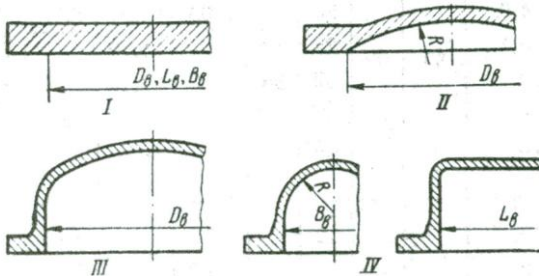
Основные типовые конструктивные формы крышек, применяемых в химических аппаратах: I – плоская (круглая, прямоугольная, фасонная); II – сферическая (круглая); III – эллиптическая (круглая); IV – цилиндрическая (прямоугольная)
